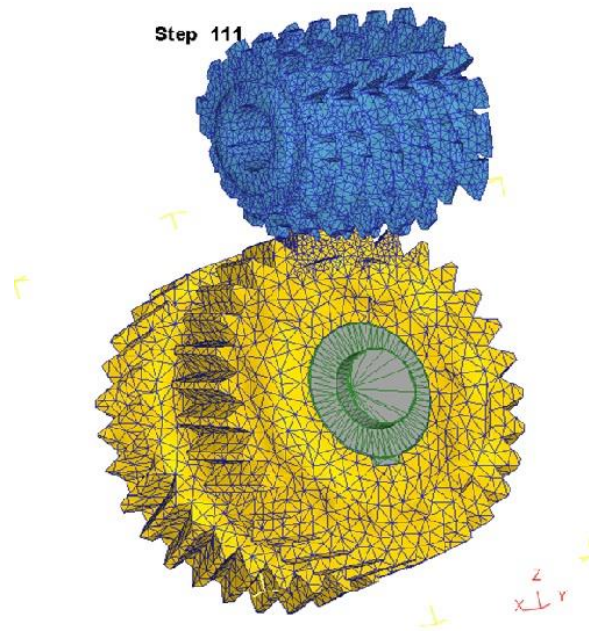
Зовнішній вигляд та розбивка 3D на елементи моделей різального інструменту та заготовки
